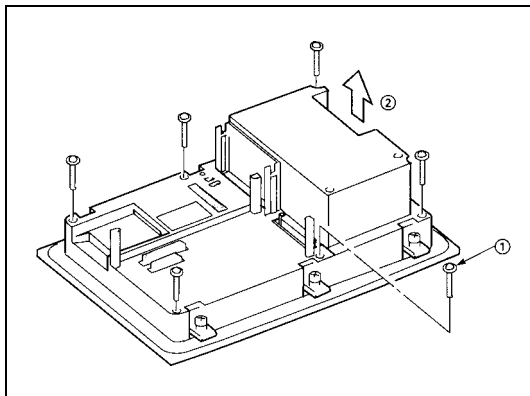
Schrauben der Rückseitenabdeckung entfernen
